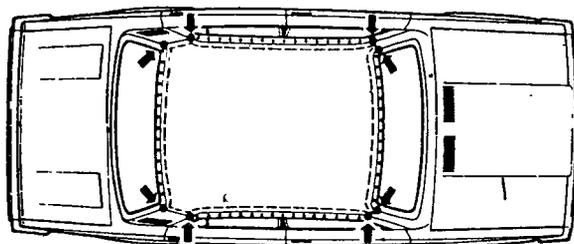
Места сварки крыши. Точками обозначены швы контактной сварки. Стрелками показаны места газовой сварки
